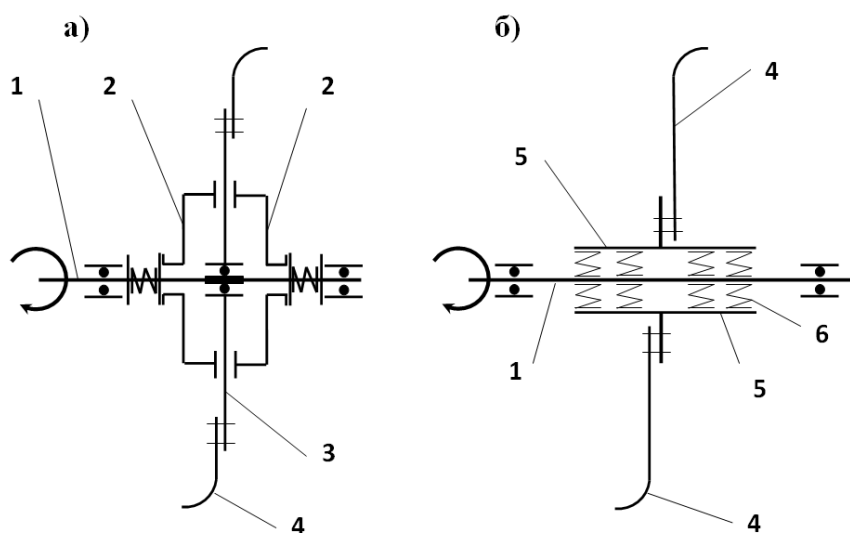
Конструктивная схема секций фрез, обходящих препятствия: а - существующая с дисковыми функциональными предохранителями; б - предложенная схема; 1 - вал барабана; левый и правый корпуса с фрикционными; 3 - диск; 4 - нож; 5 - верхняя и нижняя половинки секции; 6 - тормозные ленты закреплённые на половинках 5.
